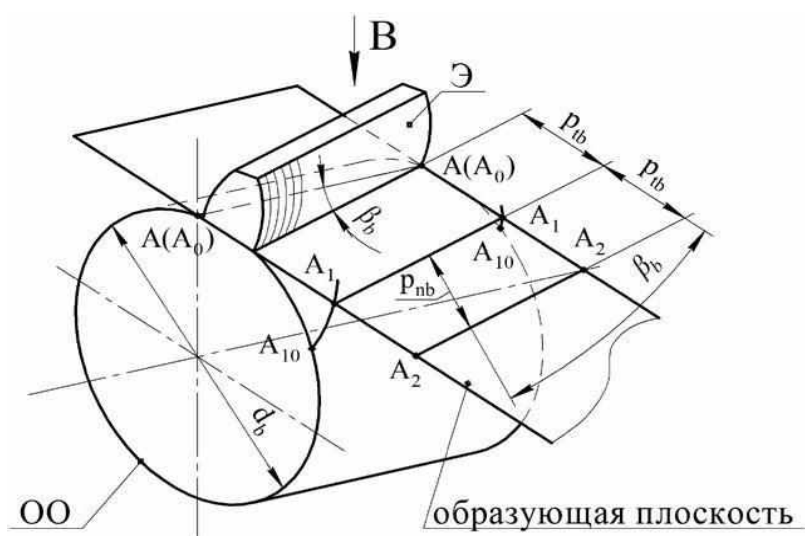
Образование рабочих поверхностей прямых зубьев цилиндрического колеса
